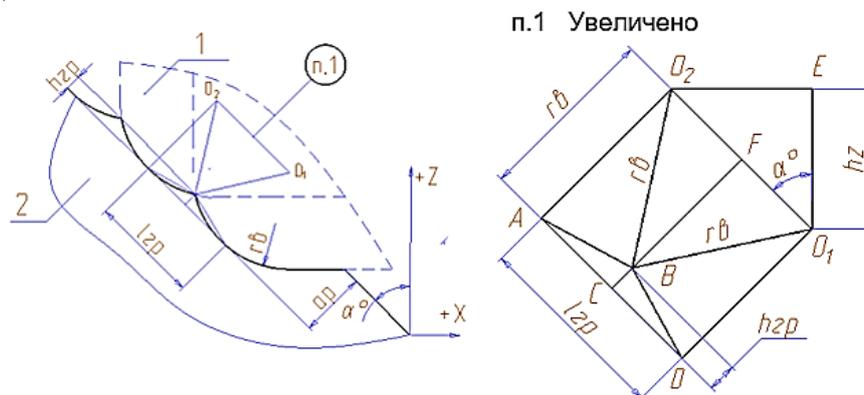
Компьютерная модель зоны контакта режущего инструмента и обрабатываемой поверхности: 1 – режущий инструмент; 2 – заготовка;  $h_z$  - шаг перемещения инструмента по оси  $Z$ , мм;  $r_0$  - радиус при вершине режущего инструмента, мм;  $\alpha^0$  - угол наклона обрабатываемой поверхности заготовки относительно оси  $Z$ , град,  $h_{гр}$  - высотное значение неровности (гребешка)
